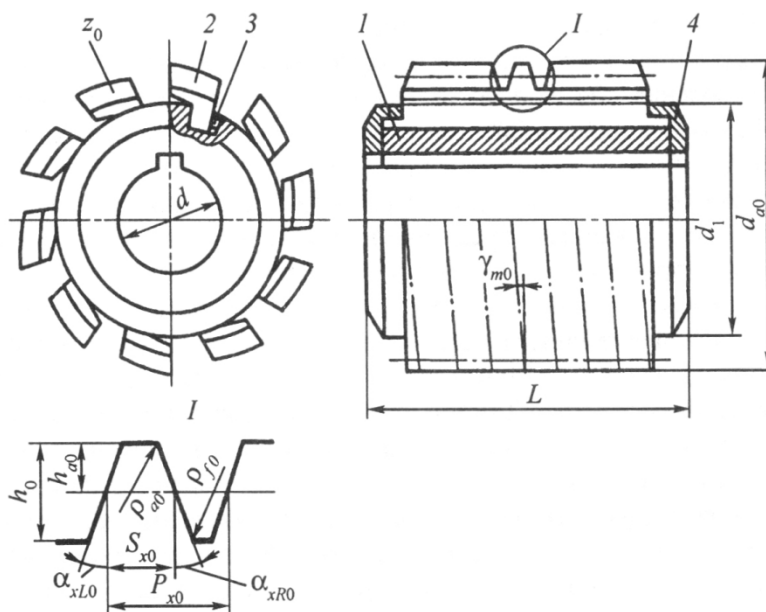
Сборная червячная фреза с поворотными рейками конструкции ВНИИ инструмента
